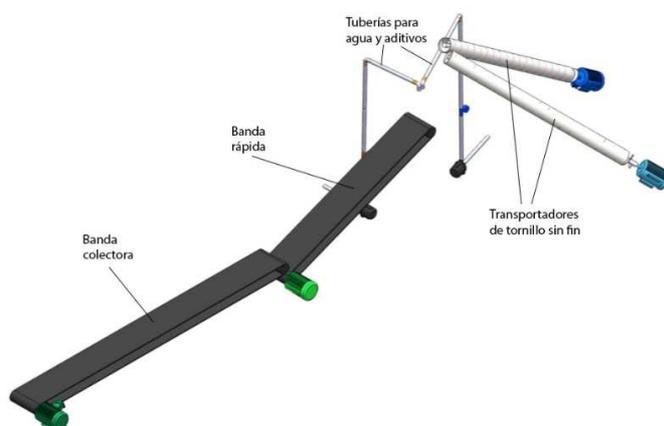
Sistema de transporte de la planta dosificadora de hormigón
